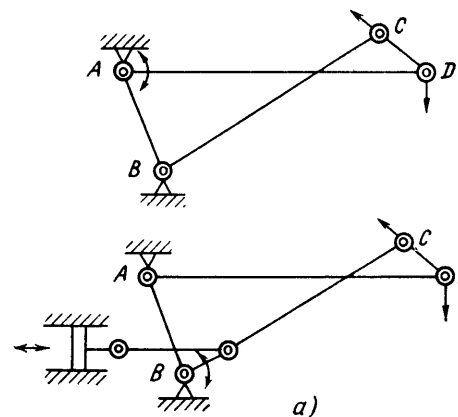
Захват с параллельным движением поверхностей, приводимый в движение гидравлическим цилиндром и реечной зубчатой передачей:
